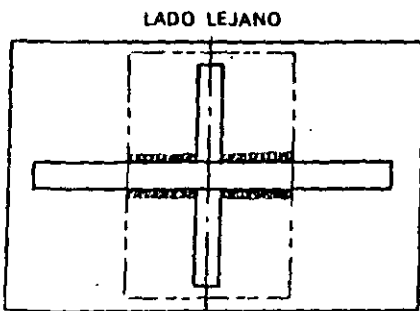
Símbolos de soldaduras en filete
